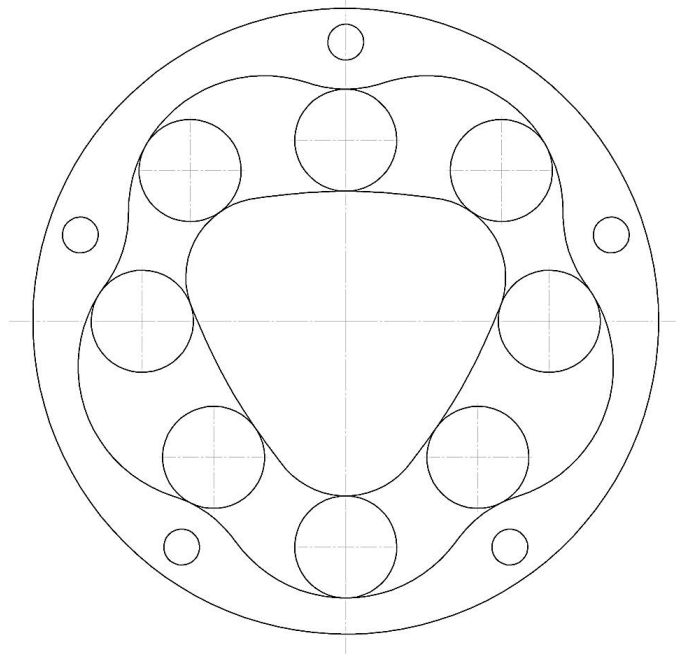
Роторный гидромотор с планетарным редуктором при сочетании арок 3x5
